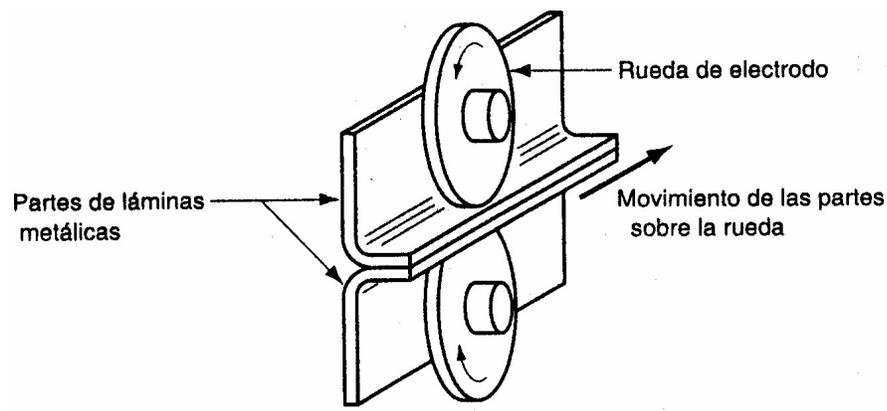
Soldadura de engargolado por resistencia (RSEW).
